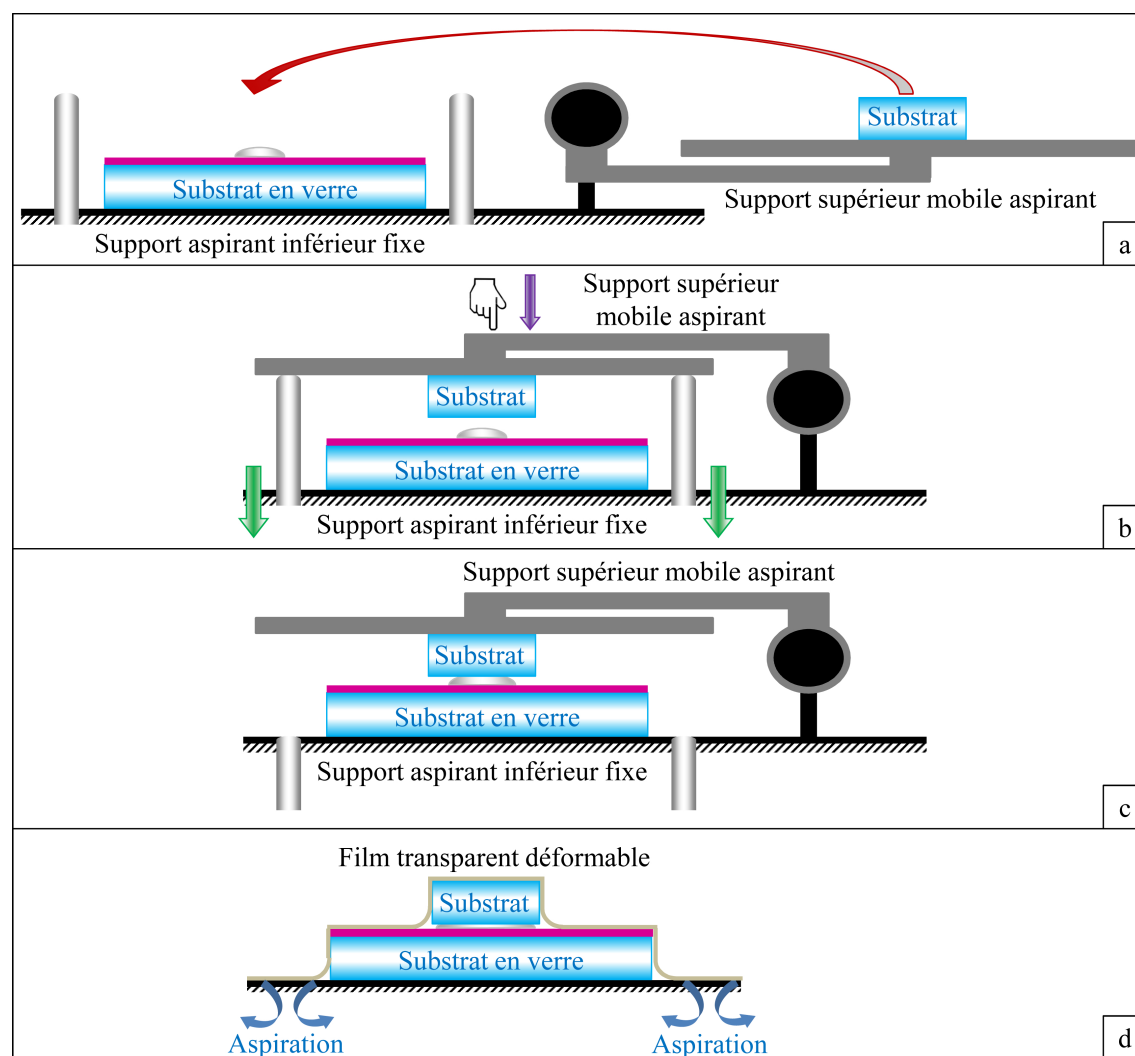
Moulage avec la machine d'assemblage de cellules
